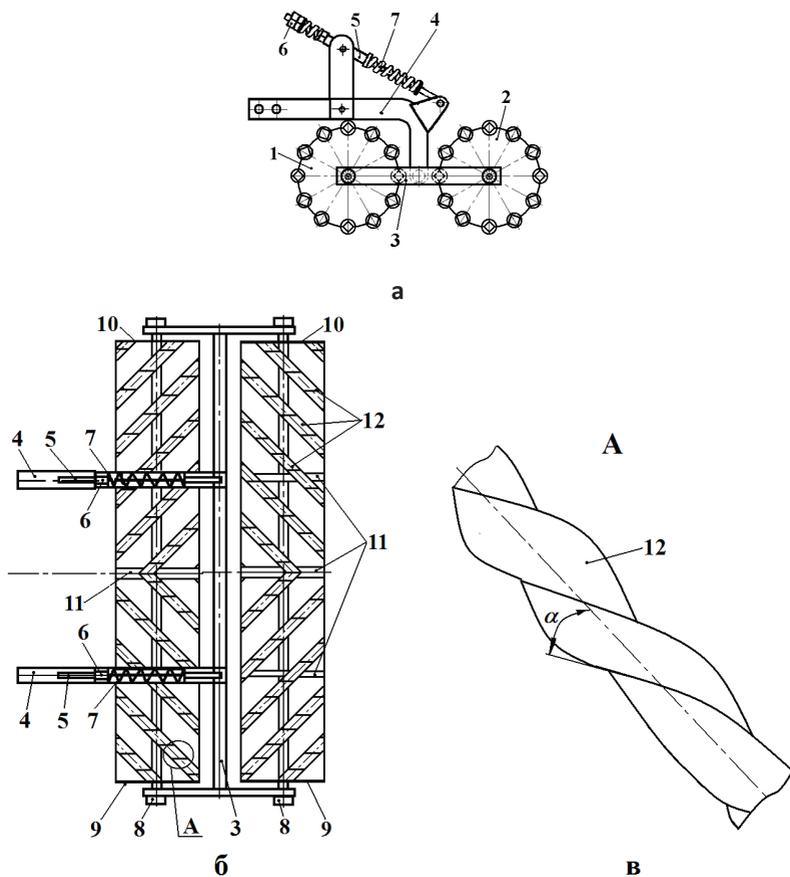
Почвообрабатывающий каток: а - вид сбоку, б - вид сверху, в - рыхлитель (вид А)
